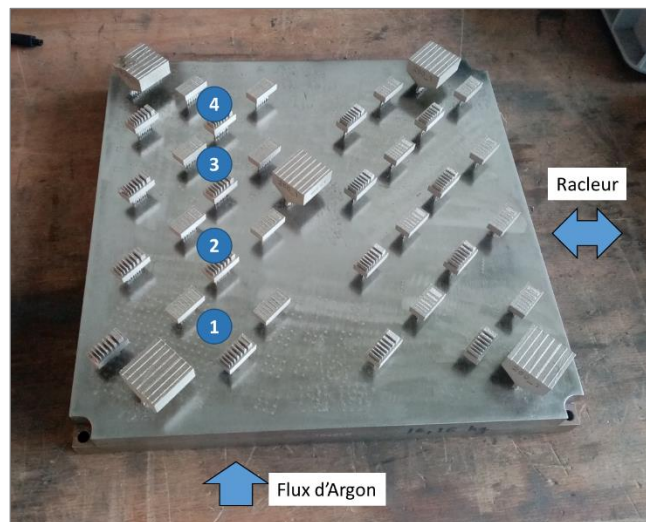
Positions des pièces sur le plateau de fabrication
